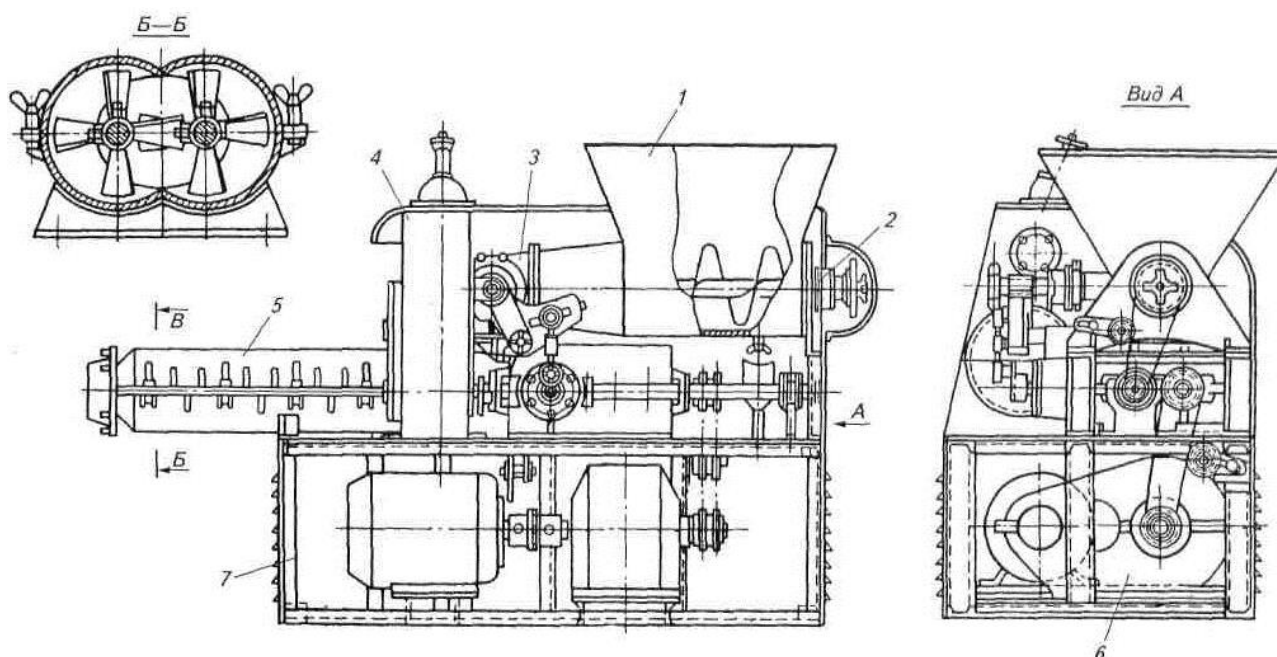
Смеситель с дозаторами обезжиренного творога и сливок: 1 - бункер; 2 - устройство для выемки шнека; 3 - дозатор творога; 4 - дозатор сливок; 5 - смеситель; 6 - привод; 7 - станина.
